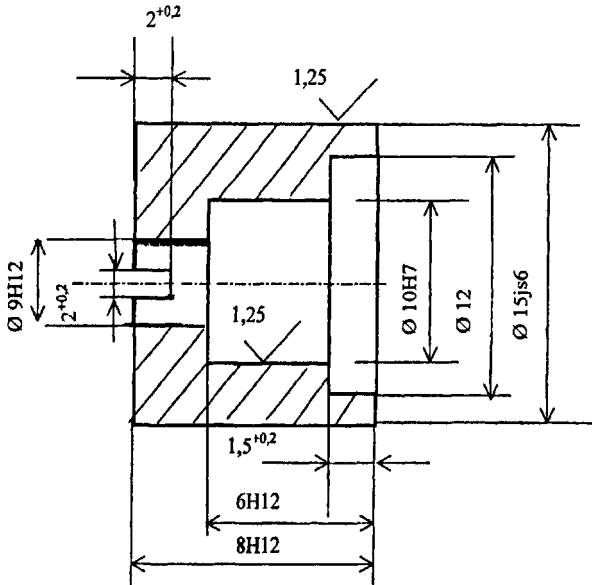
Деталь втулкообразная (гладкая цилиндрическая с двухступенчатой цилиндрической внутренней поверхностью, с пазом)
